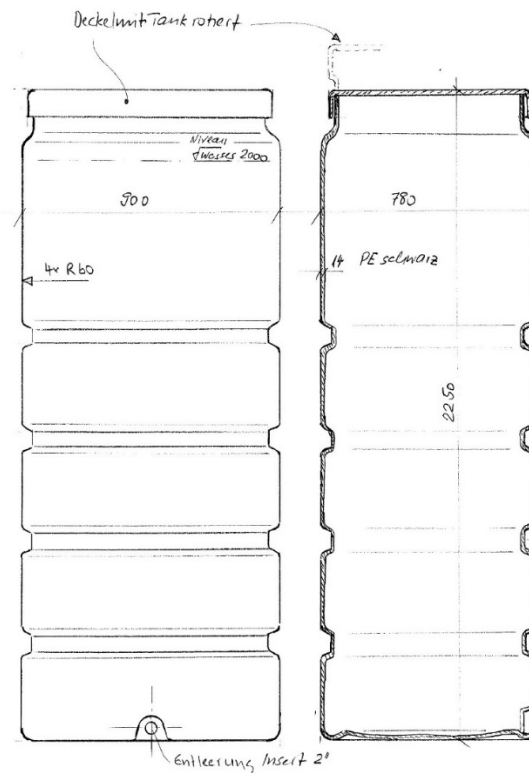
Skizze des drucklosen Kunststoffspeichers mit rechteckigem Grundriss und 1.4 m^3 Volumen. Darstellung ohne äussere Metallverstreibungen und Isolation (Quelle: Grütter Kunststoff und Formen AG).
